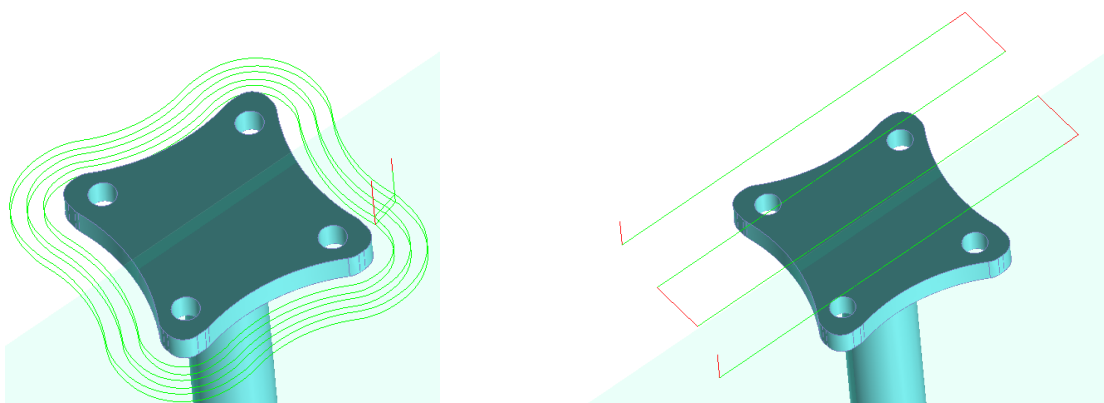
Dráhy nástrojů pro obrábění součásti prvního upnutí
